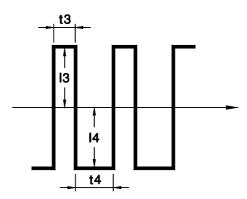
Variáveis de soldagem - Eletrodo Revestido - CA
